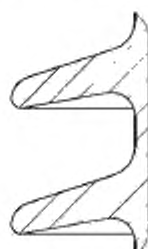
б — Стандартный профиль ребра — длинностержневые, опорные и полые изоляторы
